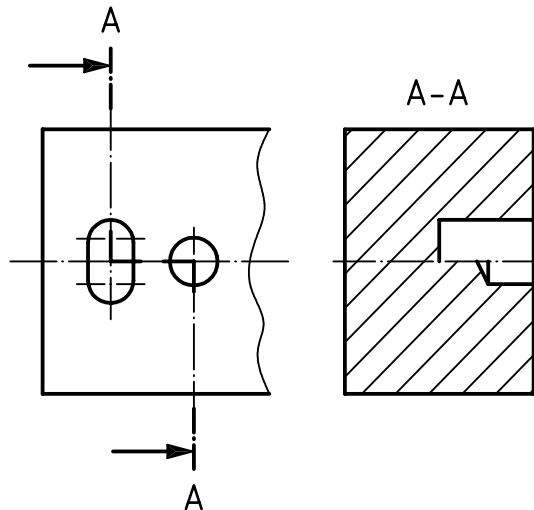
Hachures d'une section d'une même pièce coupée par des plans parallèles
